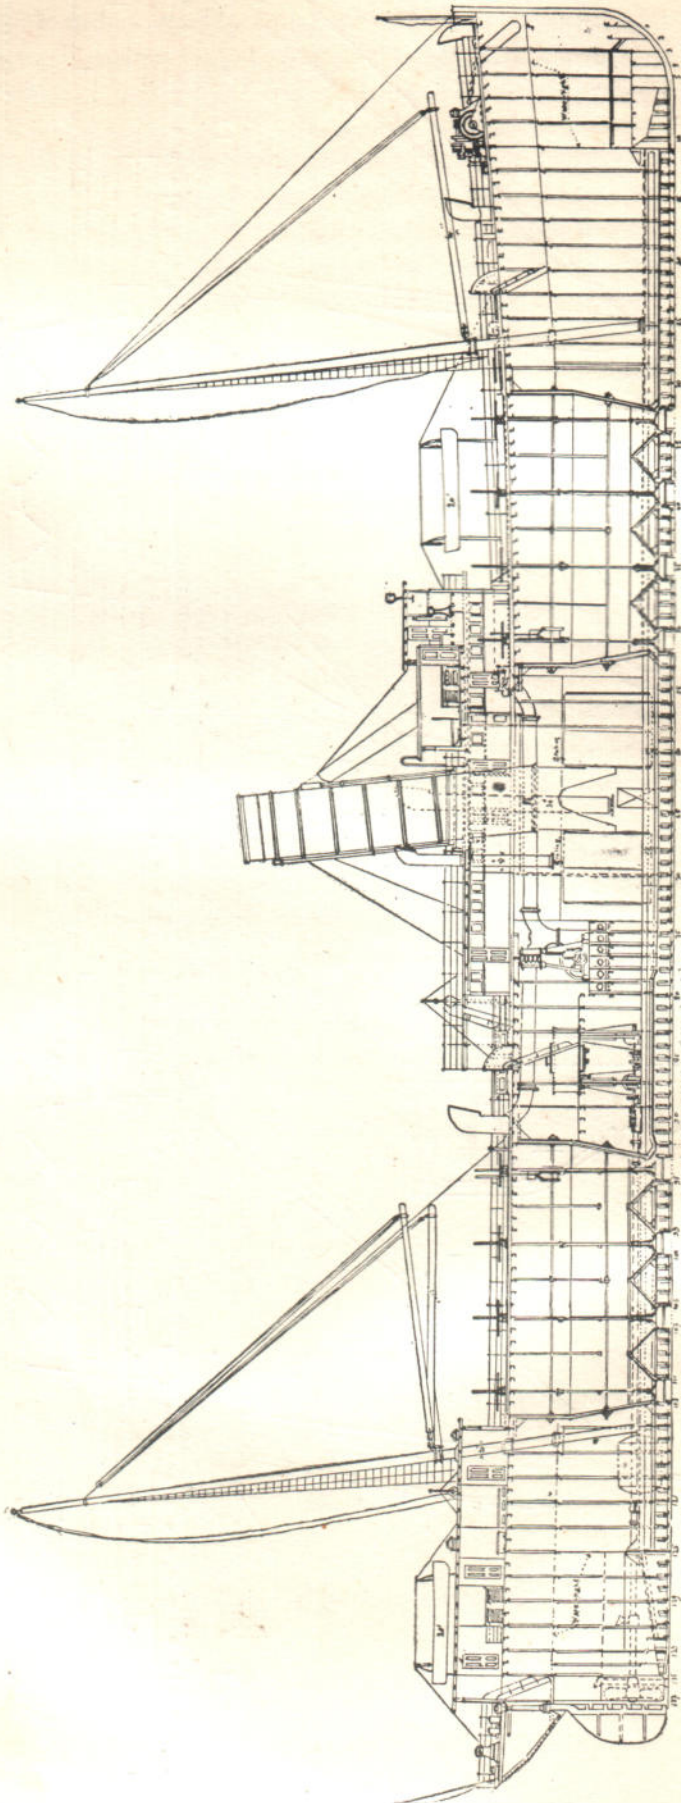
Продольный разрезь землеса, работающего на ходу.
